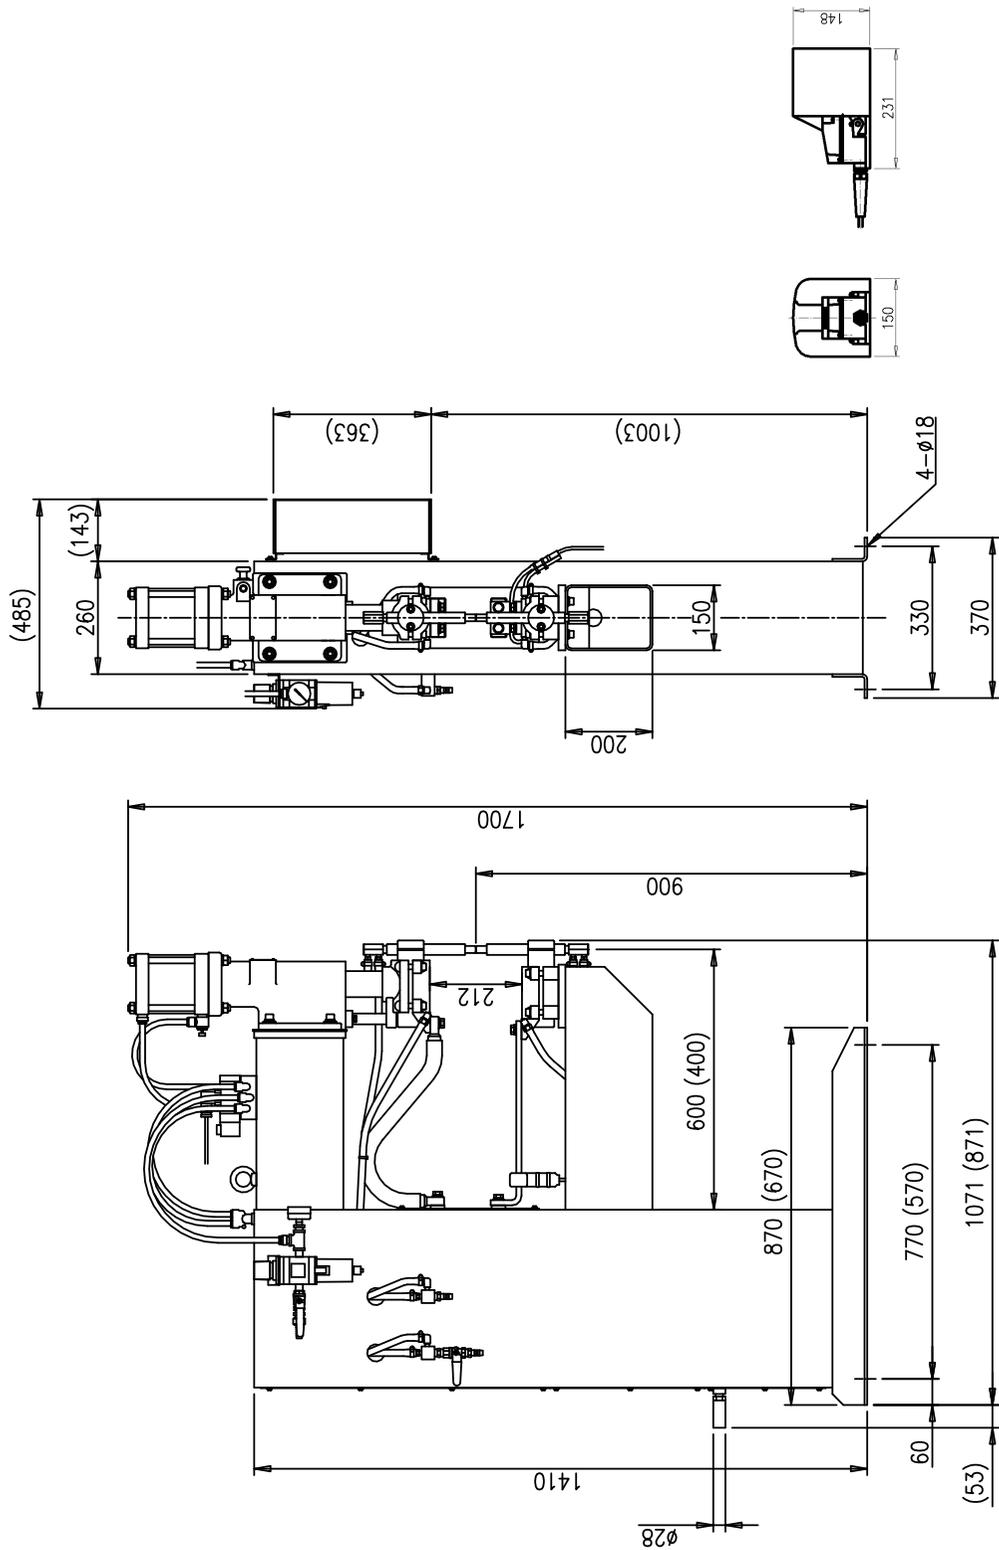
SLAJ-601シリーズ 定置式交流スポット溶接機 外形寸法図
